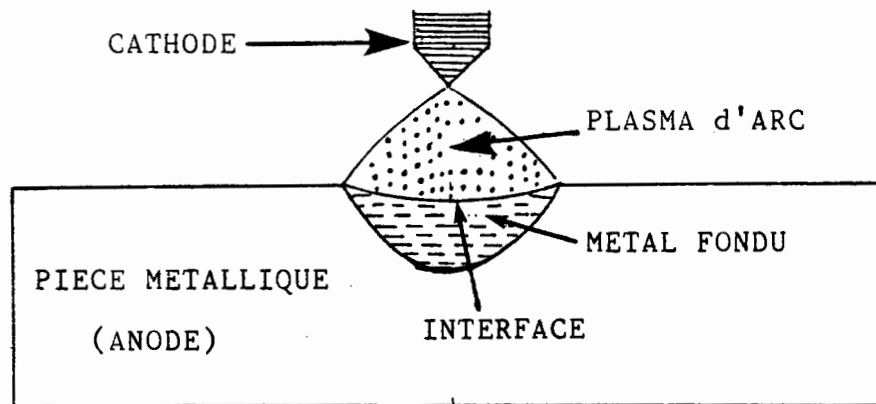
Schéma du procédé de soudure à l'arc
